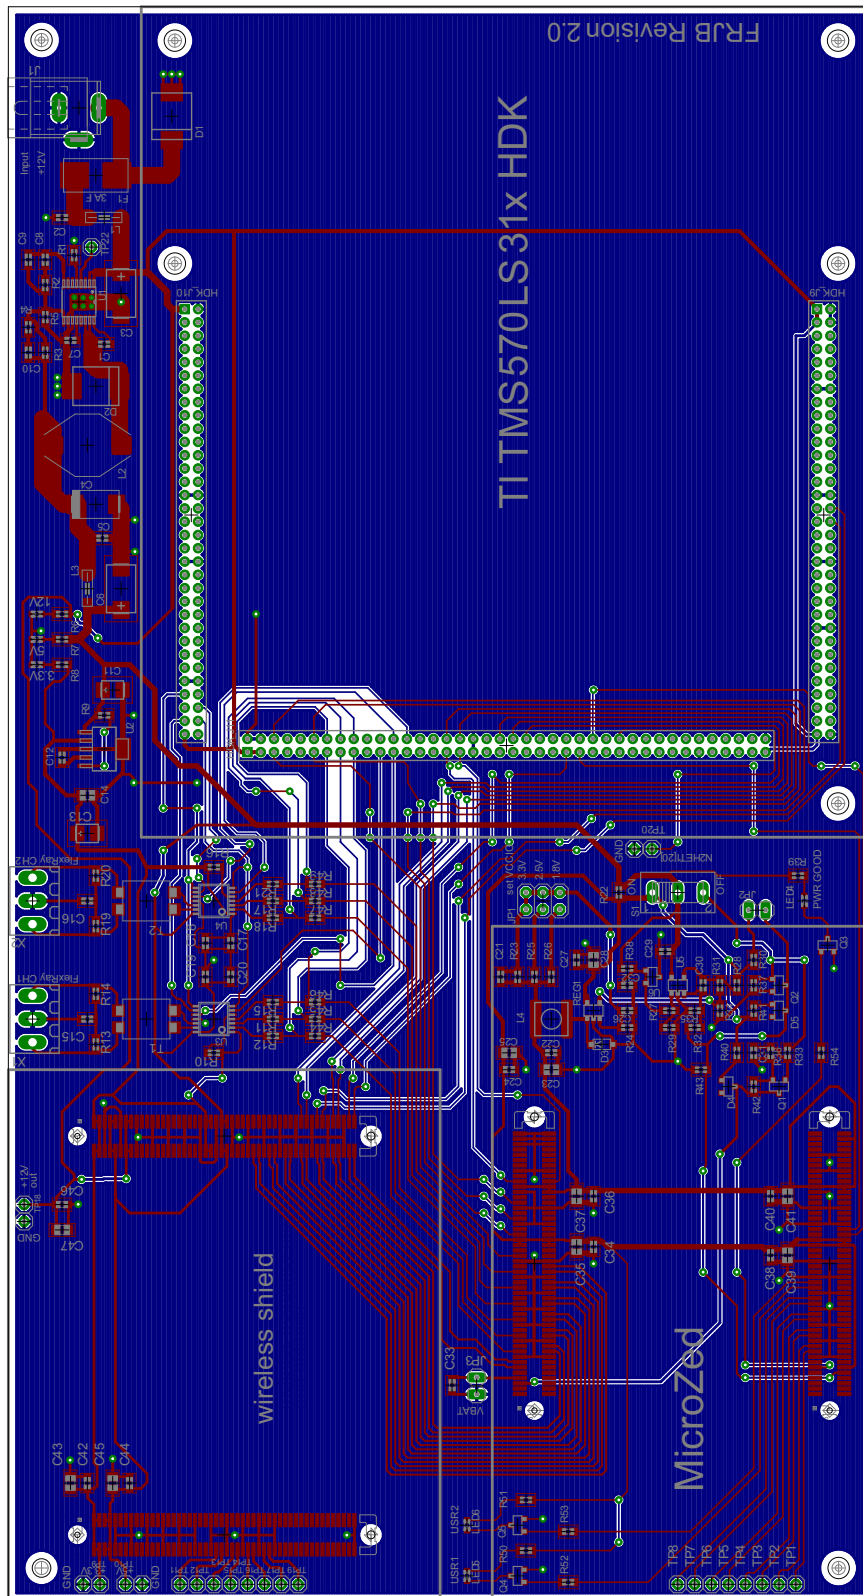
PCB Layout der Evaluierungsplattform Revision 2
